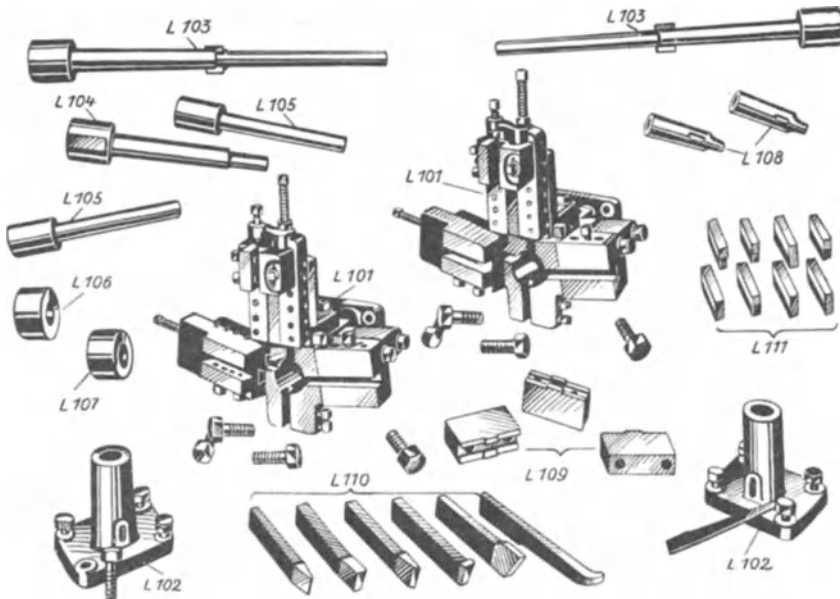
Futterwerkzeuge für schwere Revolverbänke.
